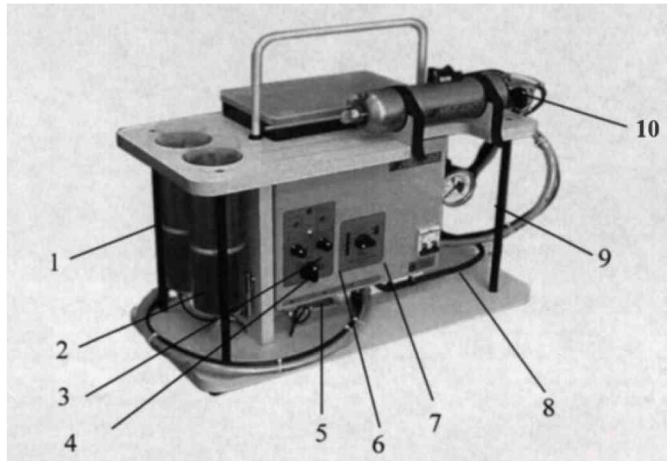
Зовнішній вигляд установки для газодинамічного напилювання ДИМЕТ моделі 403: 1 - живильник порошку для піскоструминної обробки; 2 - живильник порошку для нанесення матеріалу; 3 - тумблер включення примусового струшування; 4 - рукоятка витрати порошку піскоструйки; 5 - рукоятка перемикачів; 6 - рукоятка витрати порошку для нанесення; 7 - рукоятка перемикачів енергетичного режиму; 8 - кнопка включення установки; 9 - манометр реєстрації тиску; 10- напилювальна головка
